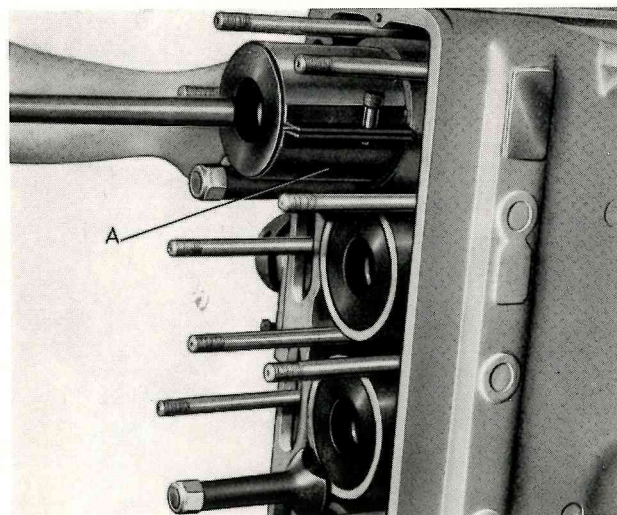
Introduzione degli stantuffi con bielle nelle canne.
